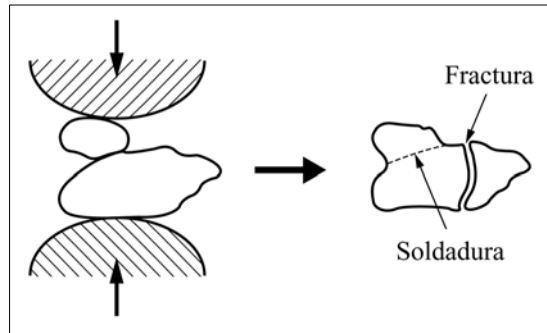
Soldaduras y fracturas sin dirección preferente.
